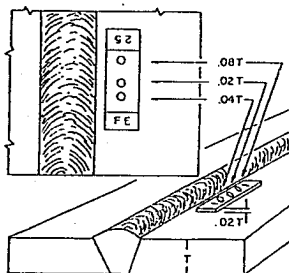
Colocación de penetrómetros durante la inspección.
